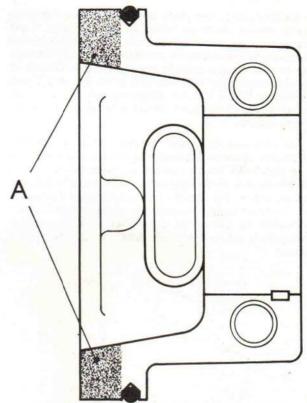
ETANCHÉÏTÉ DU JOINT DE PALIER AVANT
